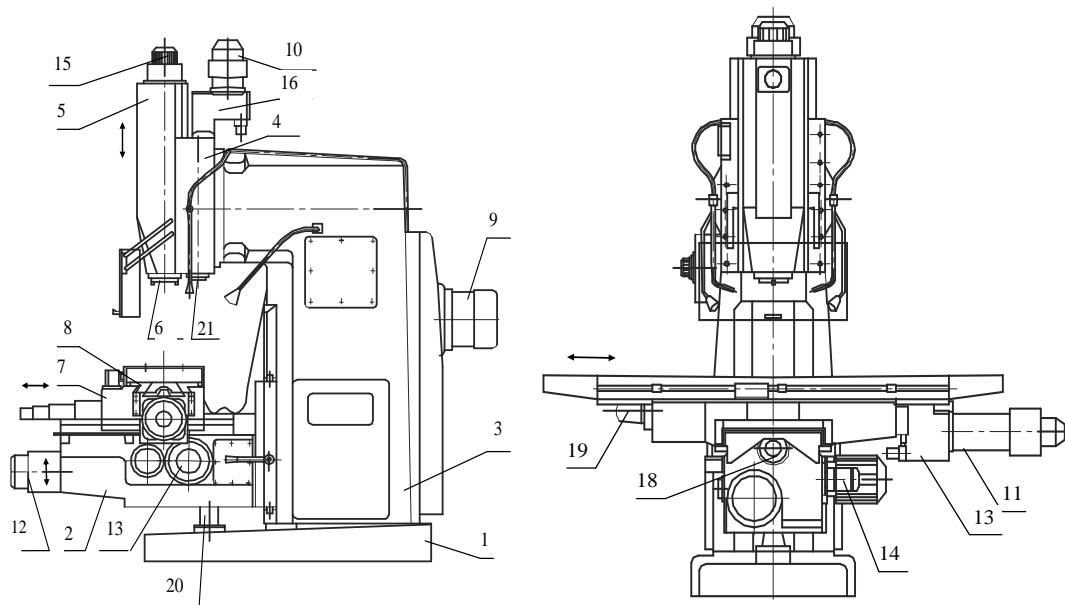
Загальний вигляд вертикально-фрезерного верстата з ЧПК мод. 6P13Ф3
